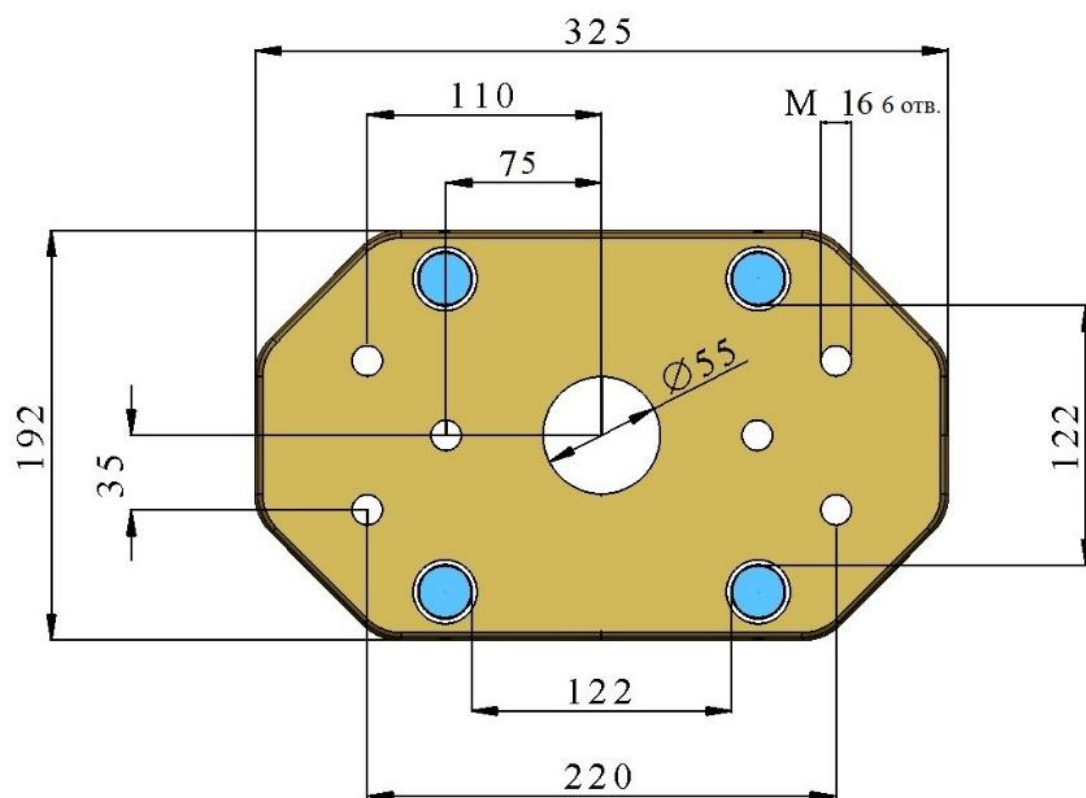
Размеры неподвижной плиты крепления станка
